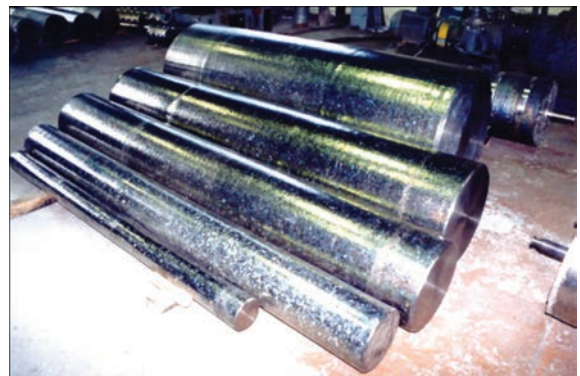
Внешний вид слитков титановых сплавов диаметром 100...600 мм с оплавленной боковой поверхностью
